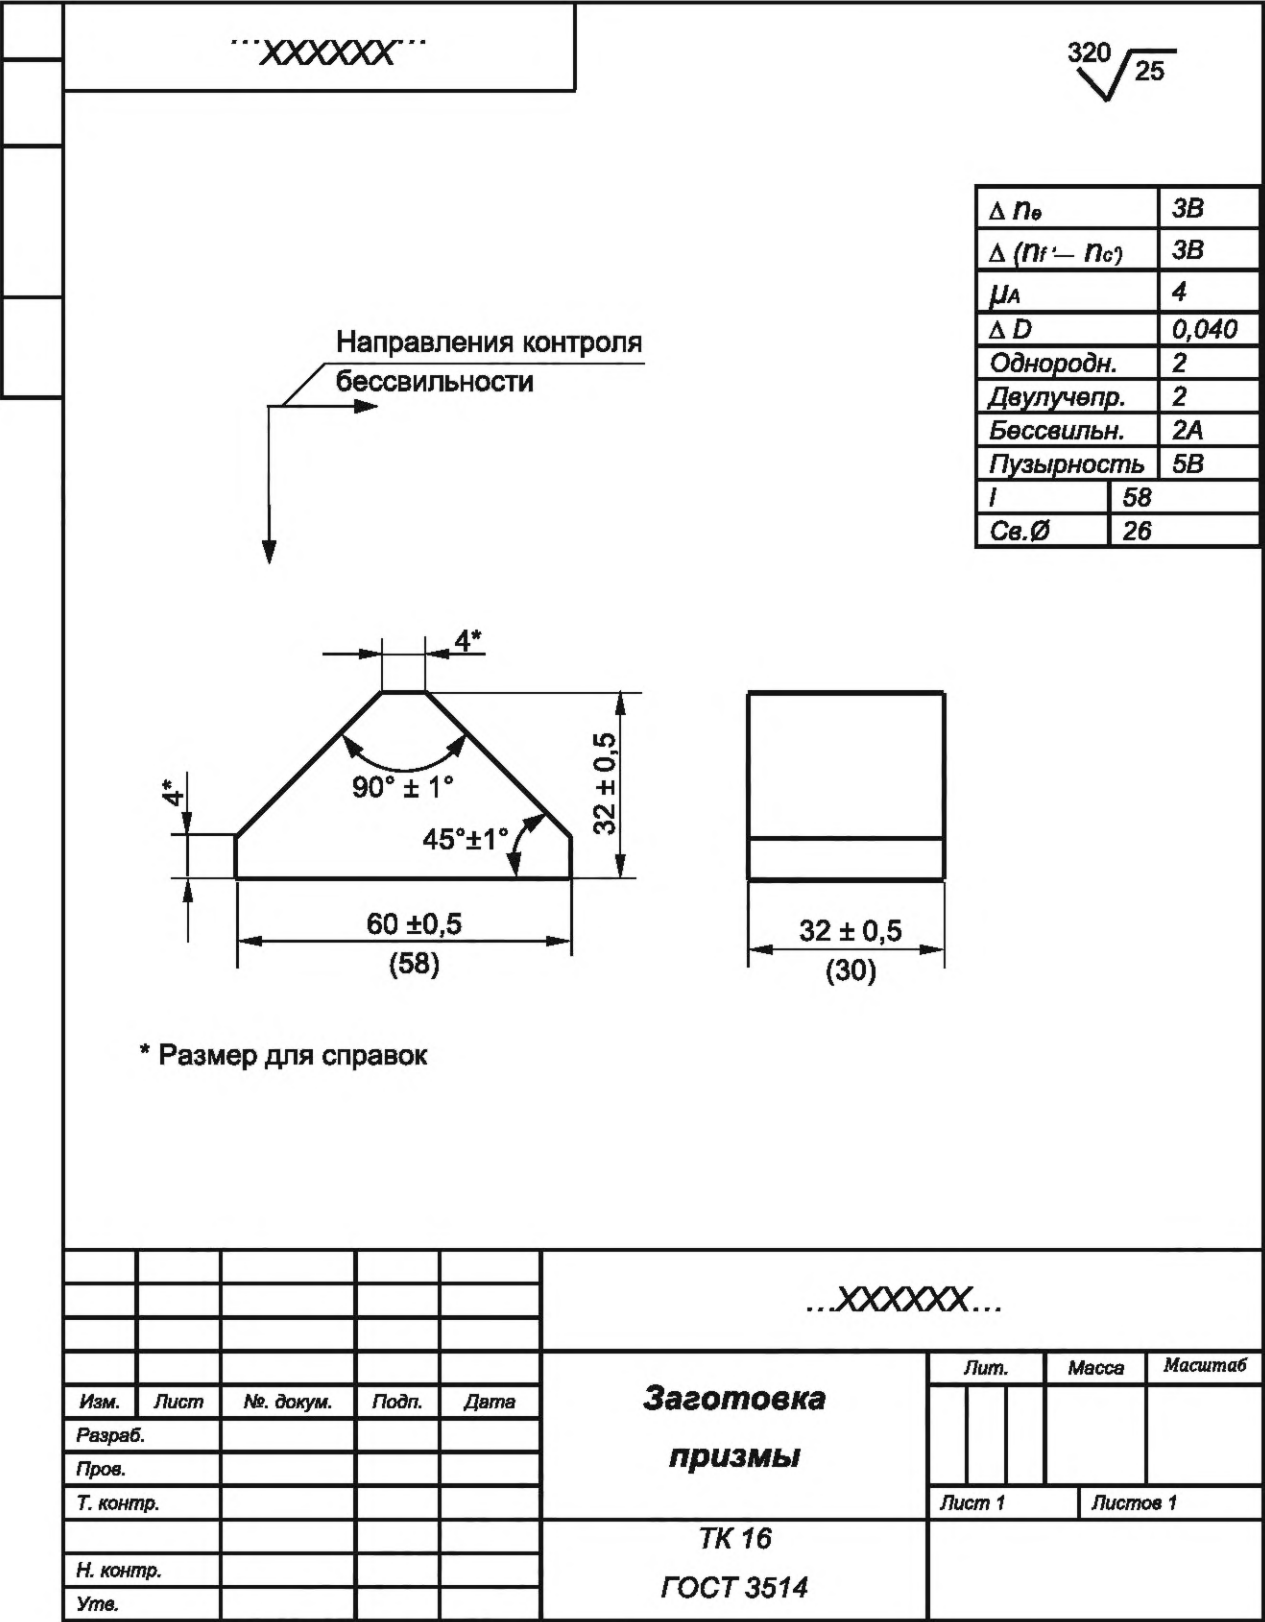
Чертеж заготовки призмы из стекла марки ТК 16 по ГОСТ 3514
